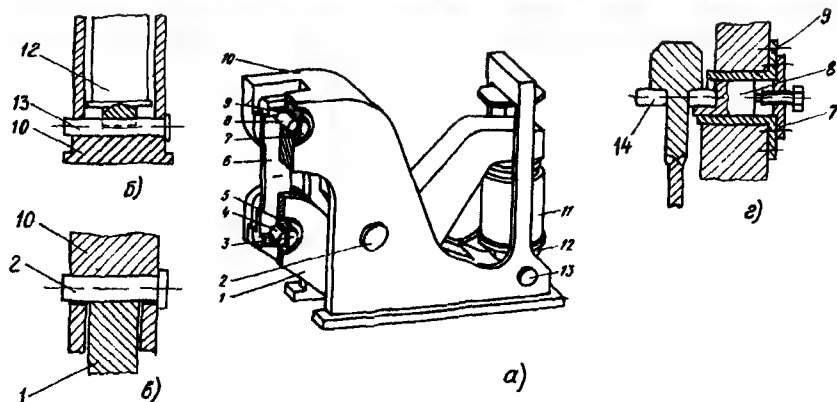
Установка для испытаний плоских толстолистовых сварных образцов с максимальным усилием 3000 кН при статическом и малоцикловом растяжении:
